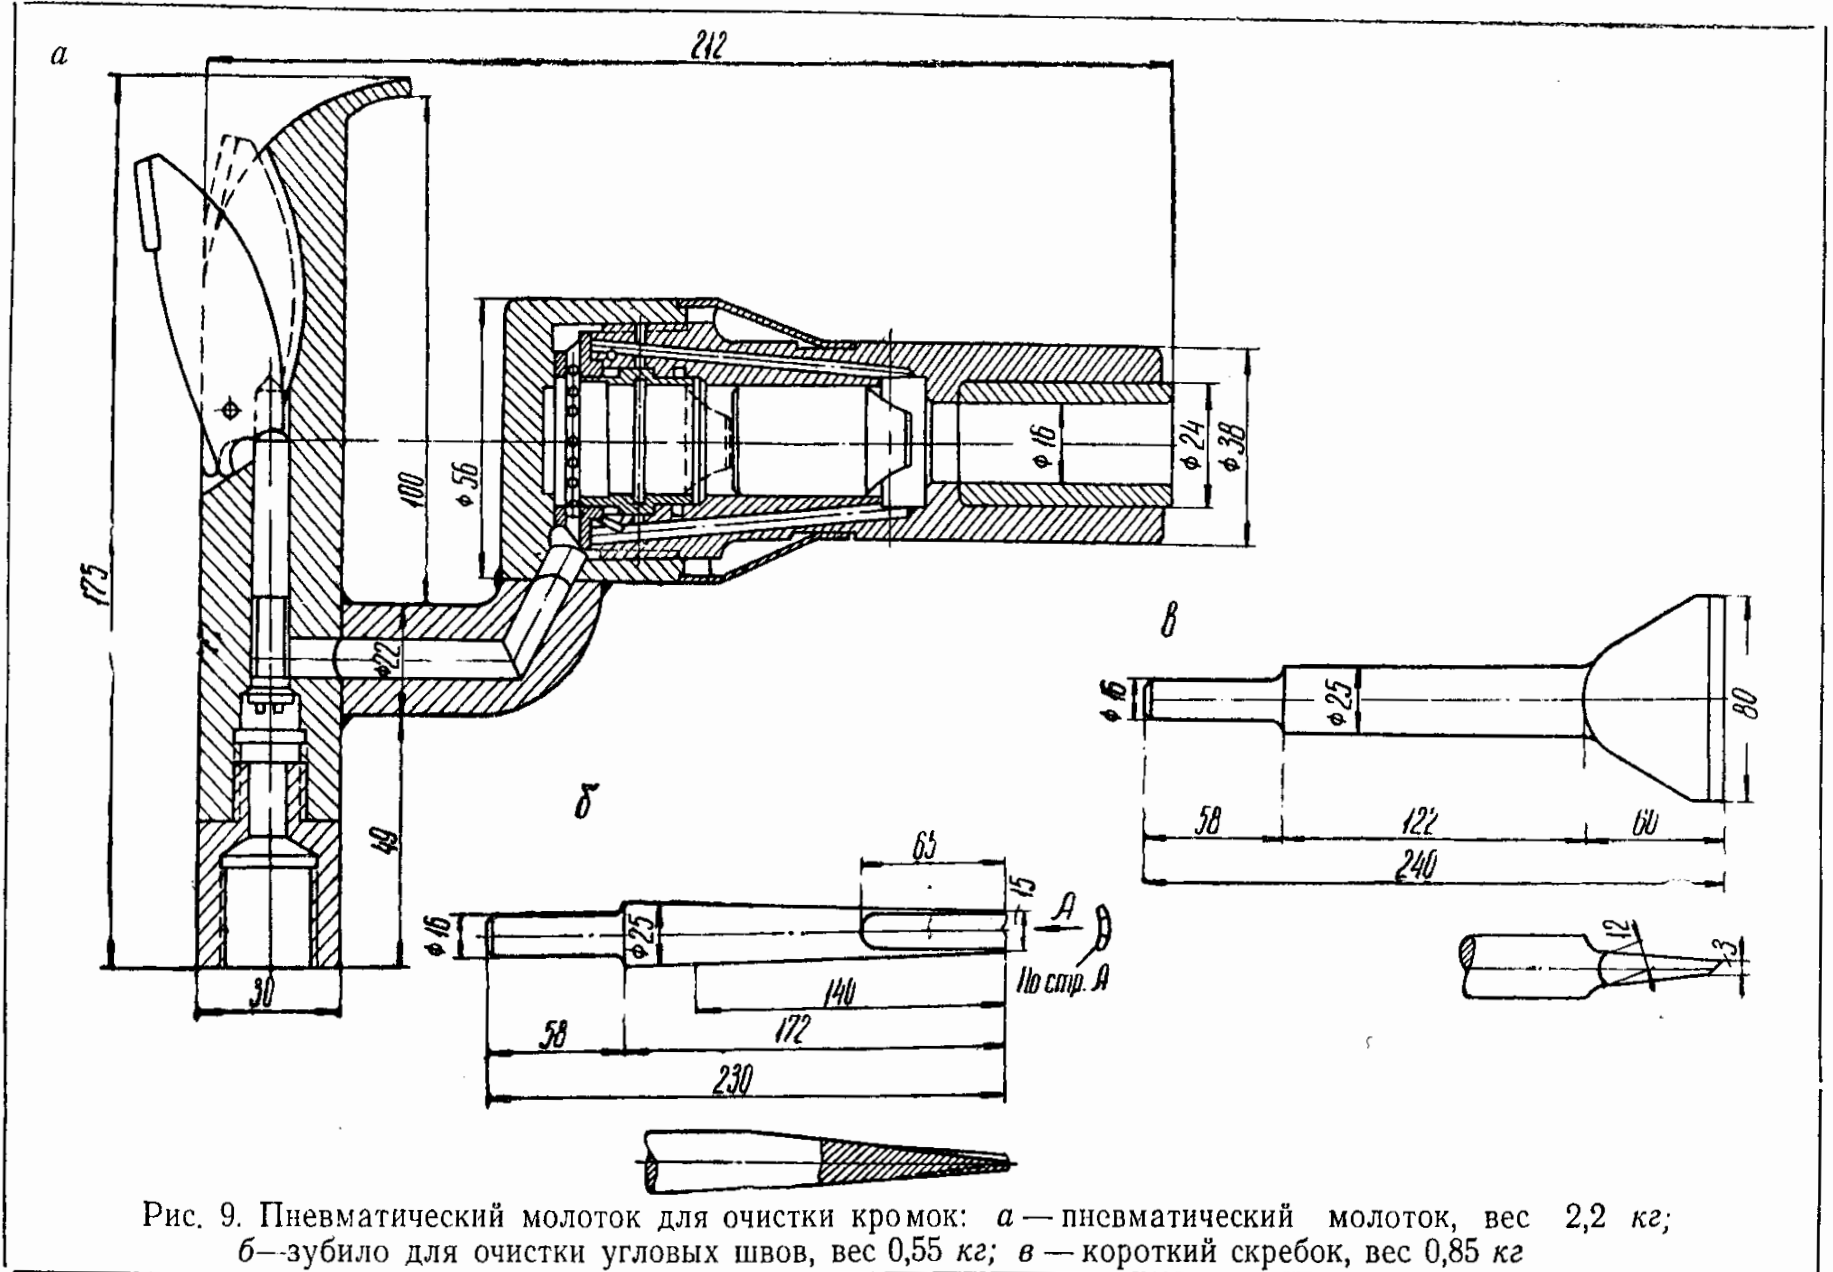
Пневматический молоток для очистки кромок: *а* — пневматический молоток, вес 2,2 кг; *б* — зубило для очистки угловых швов, вес 0,55 кг; *в* — короткий скребок, вес 0,85 кг
